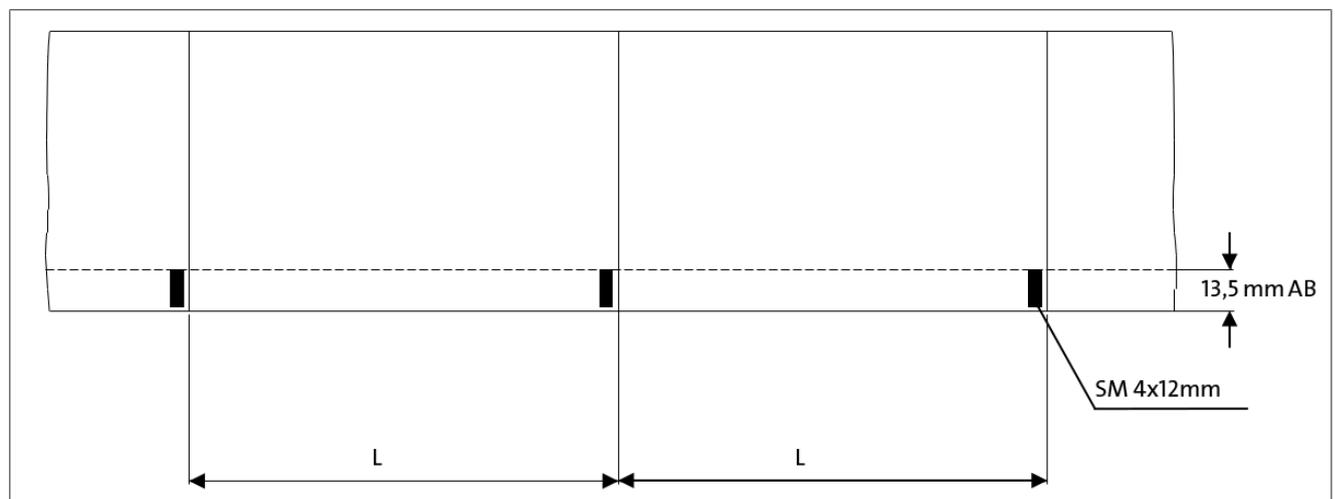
Etikettenzeichnung für Schnittmarkensteuerung
